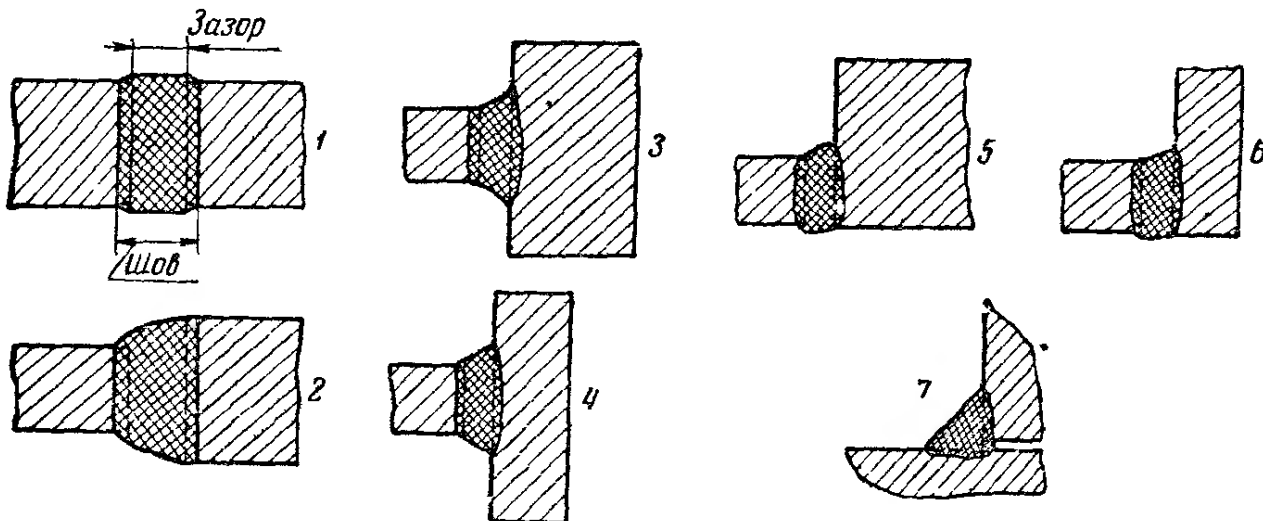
Виды соединений, выполняемых электрошлаковой сваркой:
